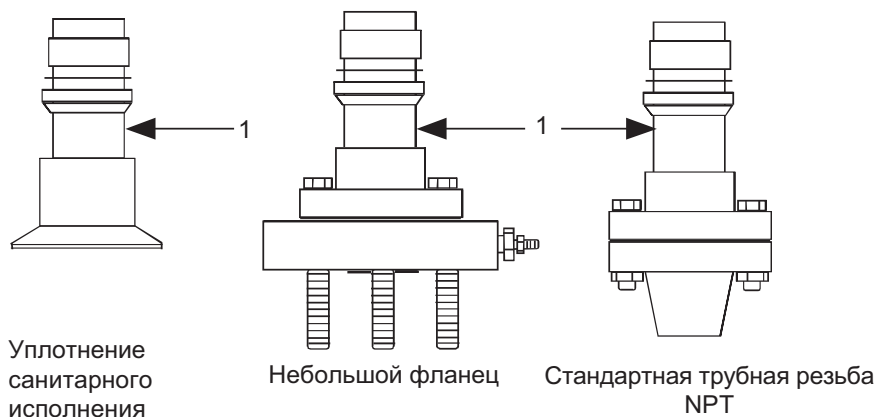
Корпус датчика преобразователя для высокой температуры
